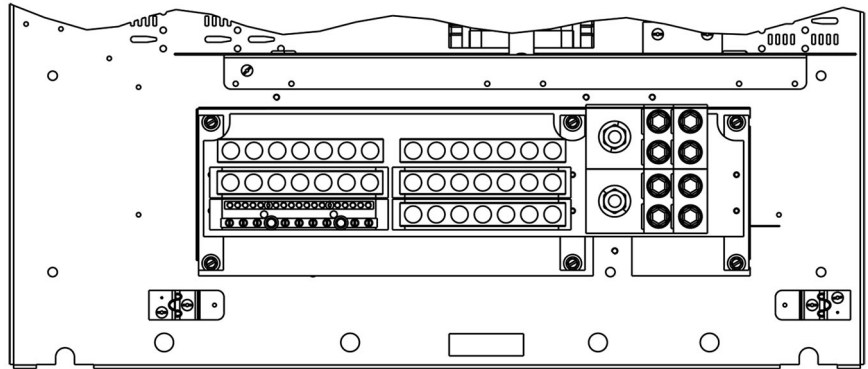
Emplacement de l'installation du neutre sur des panneaux HCR-U (cosses principales à gauche et barres du neutre à droite)
